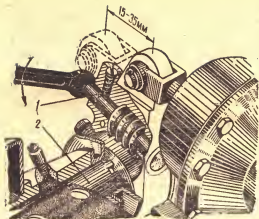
Регулировка зазора между колодками и барабаном автомобиля ЗИЛ-164:
